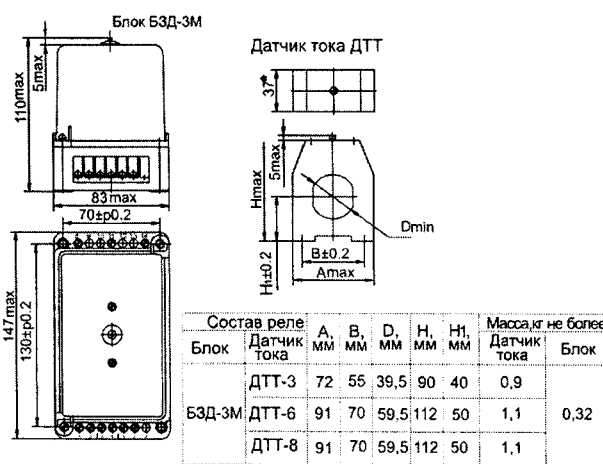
Габаритные и установочные размеры реле РЗД-3М4 (5; 6)
